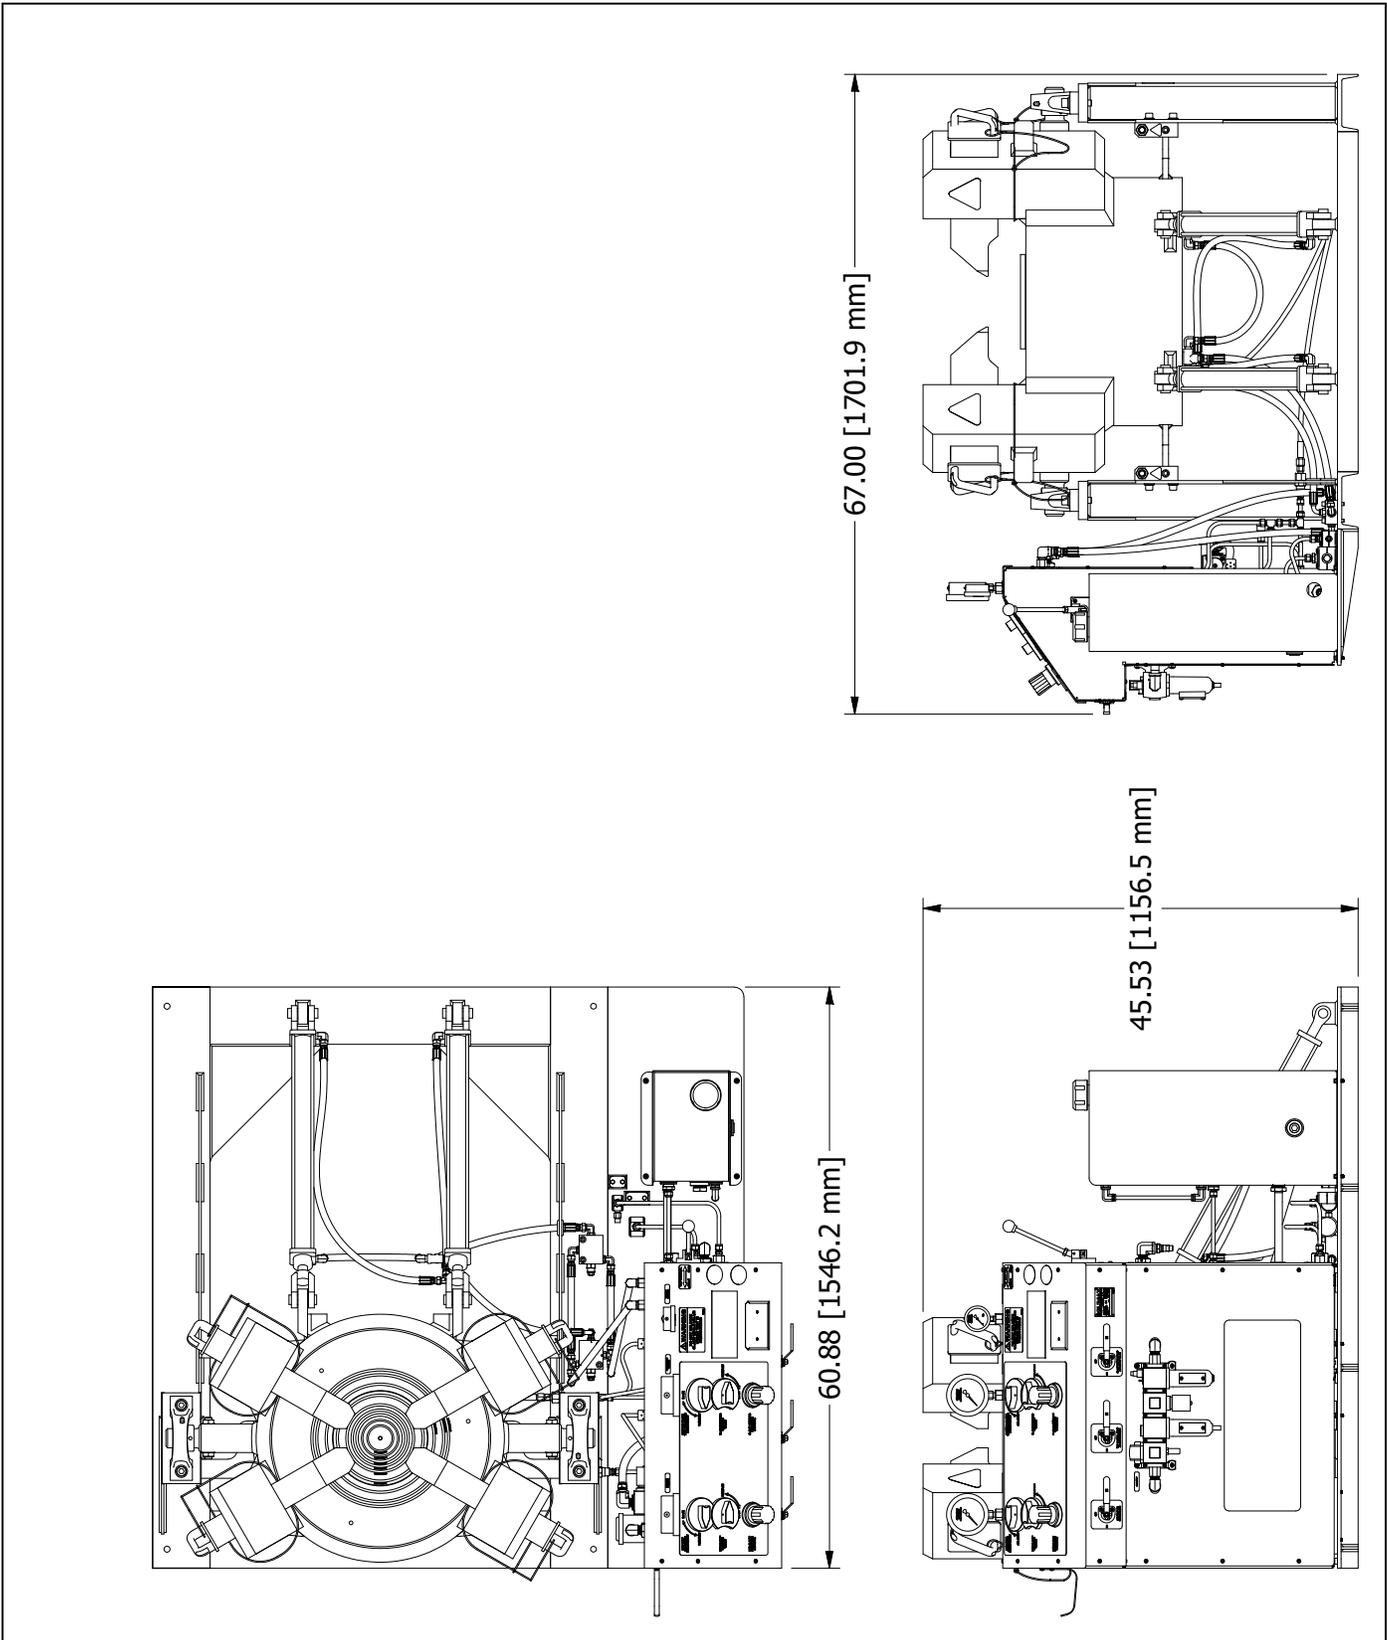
DIMENSIONES DE LA MORDAZA
